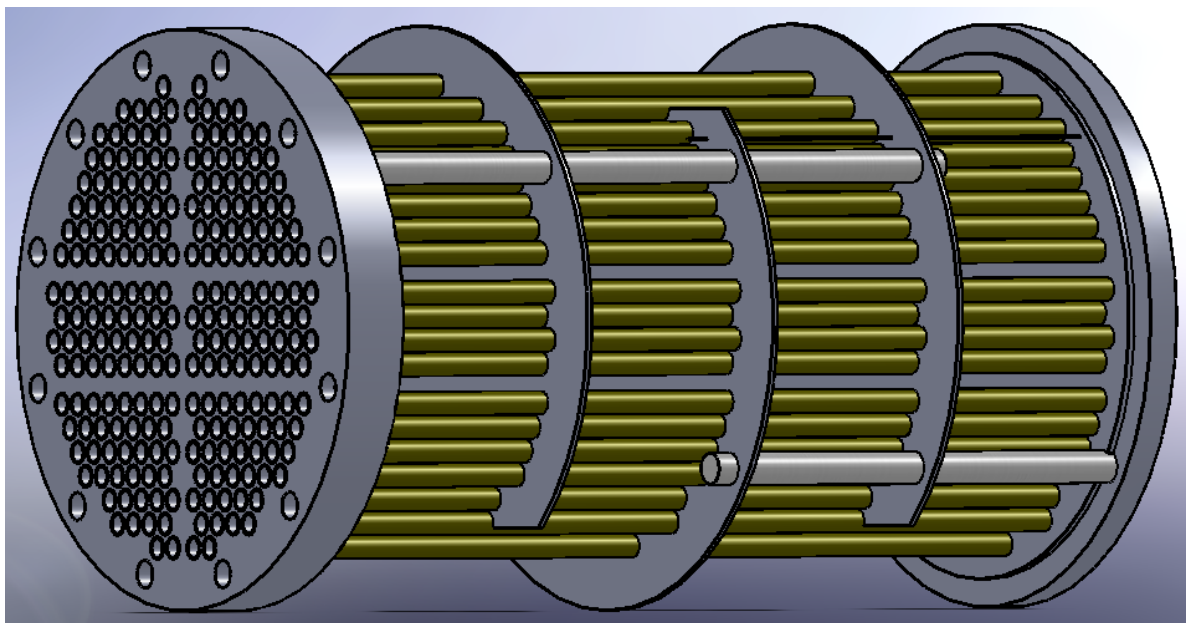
Desenho isométrico do feixe tubular do trocador de calor
